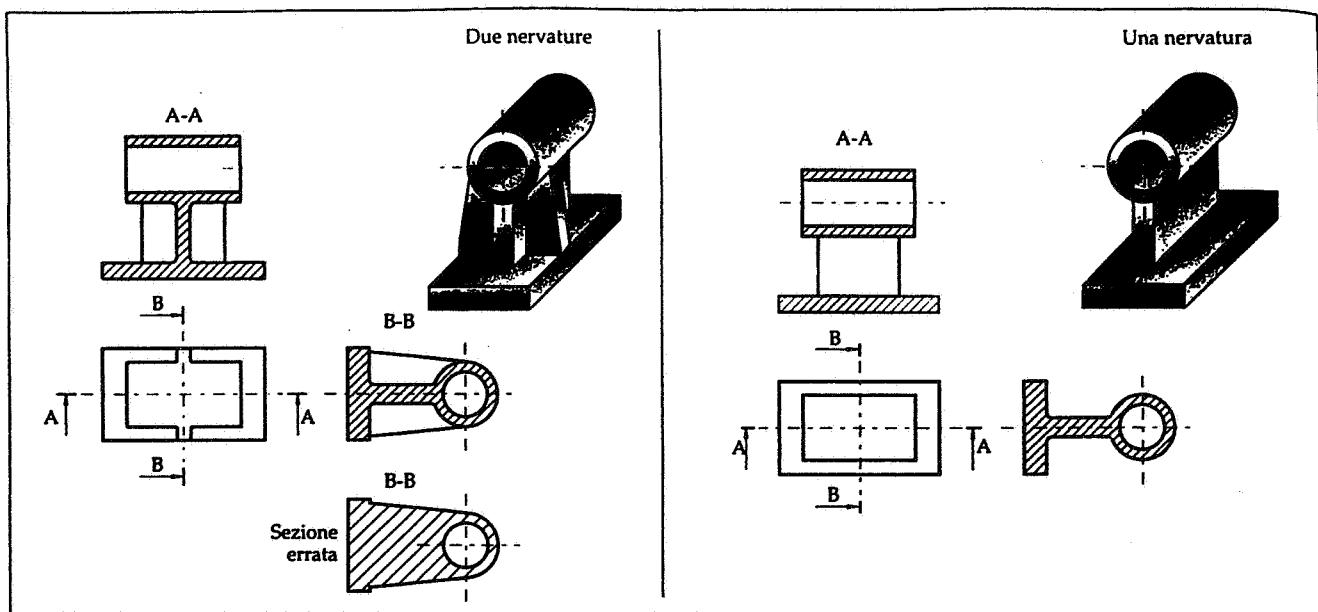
Le nervature parallele al piano di rappresentazione non si sezionano.
